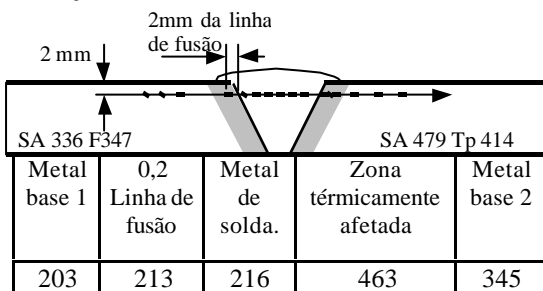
Perfil da dureza vickers HV10, junta dissimilar soldada com ERNiCr-3,.
